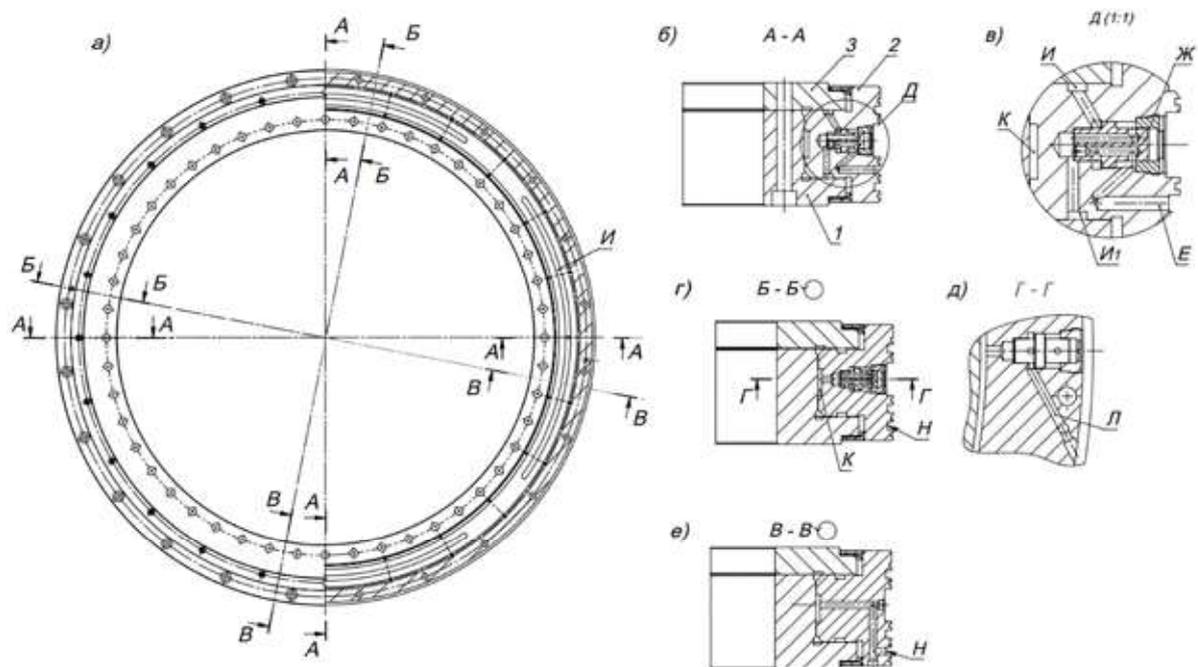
Гидростатическая опора с регулируемым давлением подачи рабочей жидкости: -а) вид сверху; -б) вид А-А; -в) вид Д; -г) вид Б-Б; -д) вид Г-Г; -е) вид В-В
